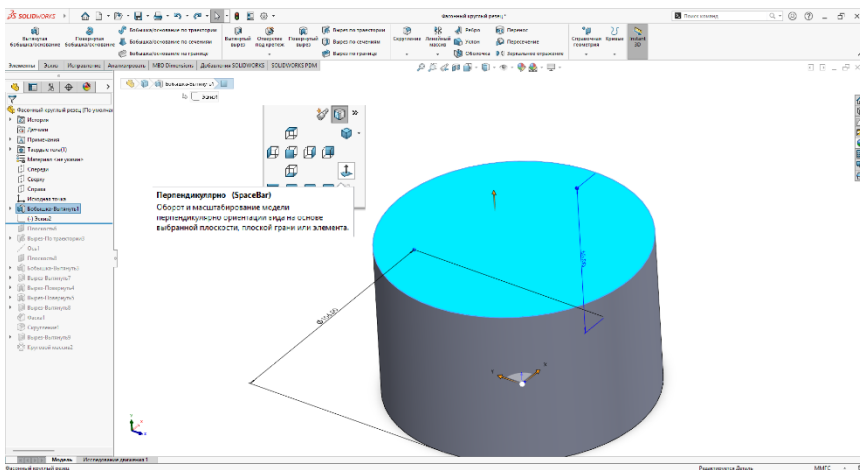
Расположение торцевой поверхности цилиндрической заготовки перпендикулярно взгляду
